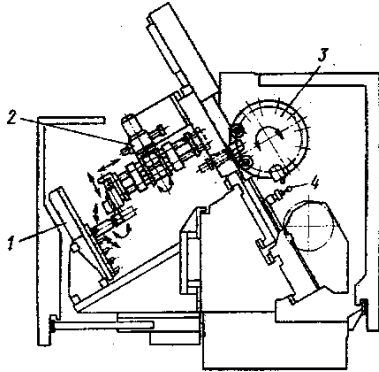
Схема токарного станка с ЧПУ и устройством автоматической смены резцовых головок
